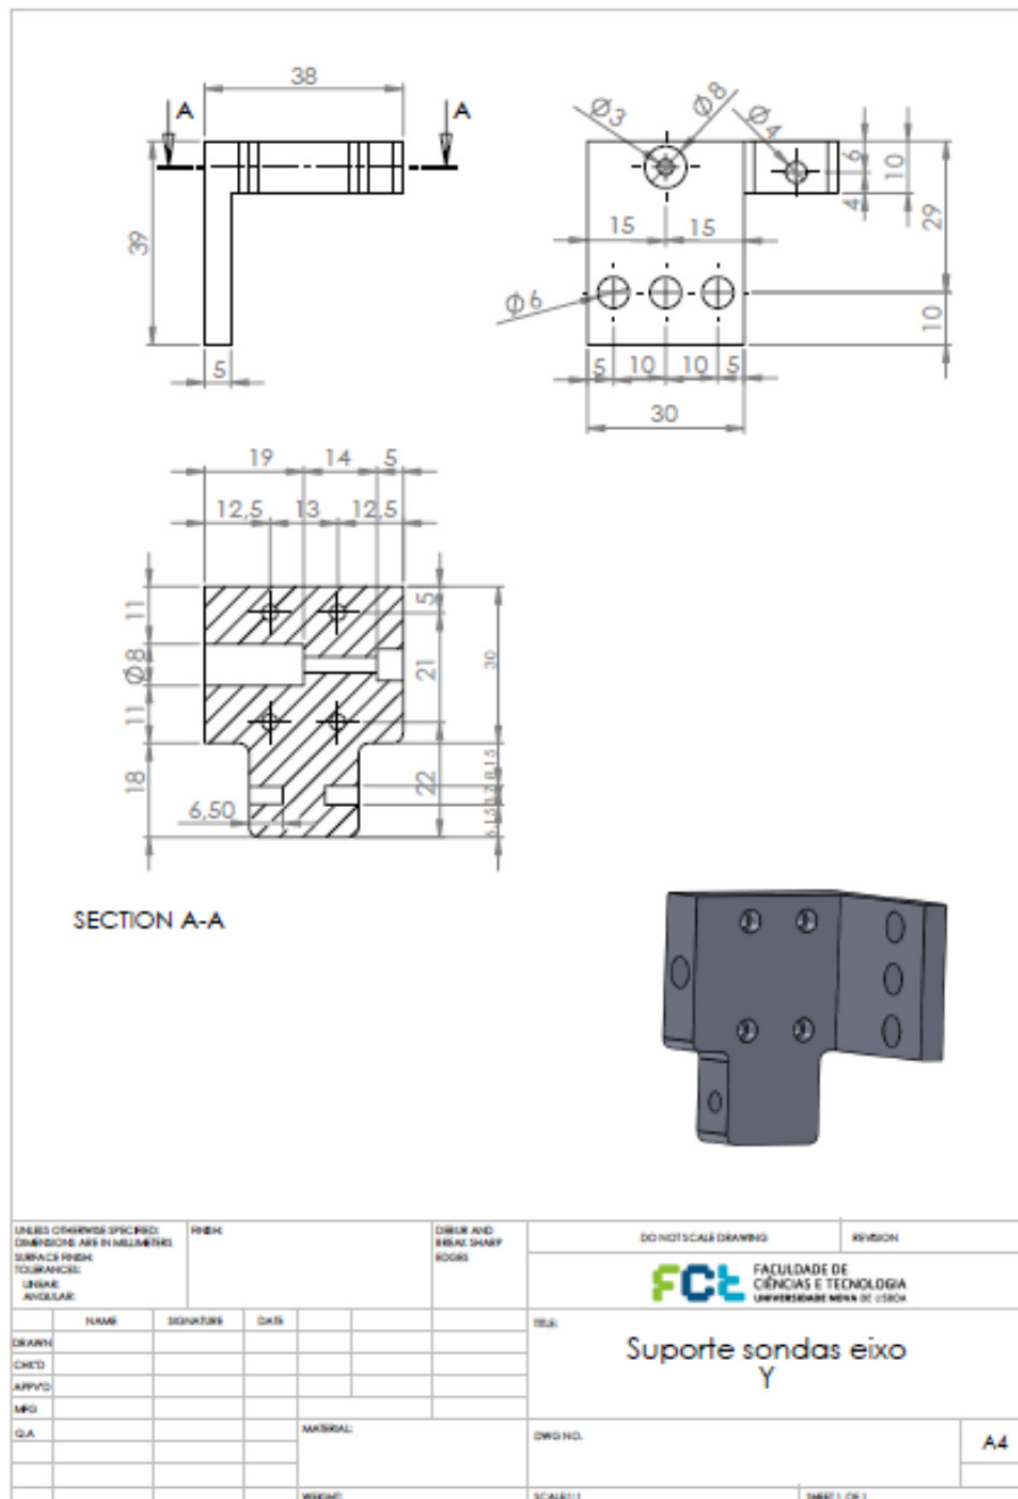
Desenho técnico do suporte das sondas para o eixo Y
